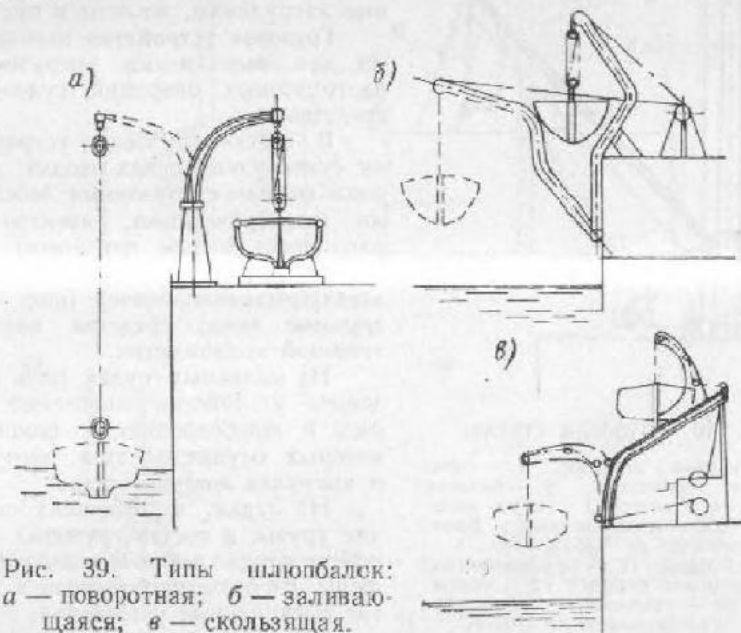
Типы шлюпбалок: а — поворотная; б — заливающаяся; в — скользящая.
